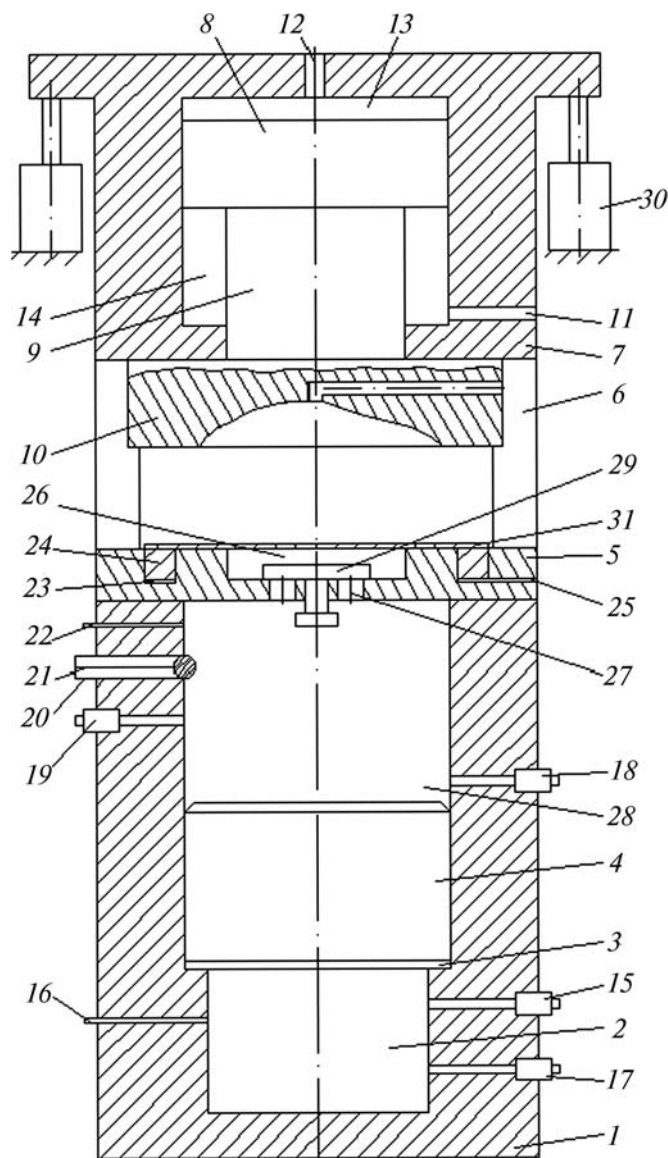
Схема двухкамерного пресса для листовой штамповки:
